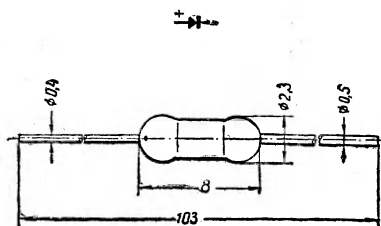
Габаритный чертеж дисков типа Д1, Д9
